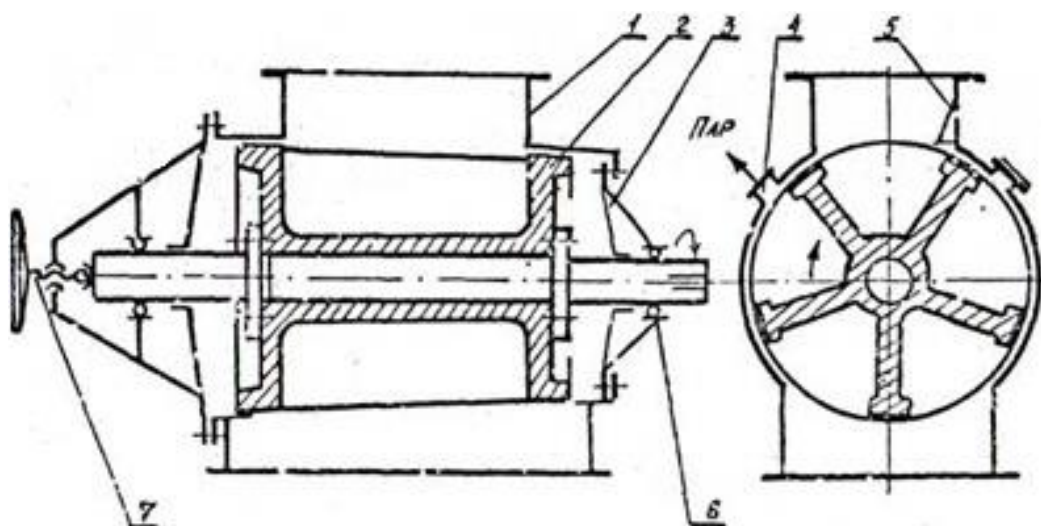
Питатель низкого давления: 1-корпус; 2-ротор; 3-крышка; 4-патрубок для отвода пара из карманов ротора; 5-шабер; 6-подшипник; 7-механизм присадки ротора
